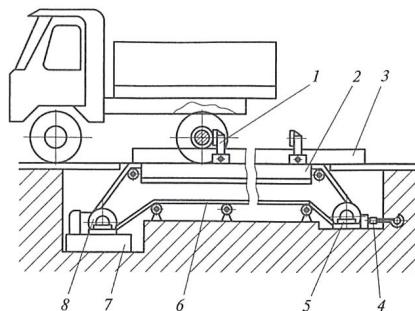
Схема толкающего конвейера: 1 – толкатель; 2 – направляющие пути тягового органа; 3 – колесоотбойник; 4 – натяжной механизм; 5 – натяжная станция; 6 – тяговый орган; 7 – приводная станция; 8 – ведущая звездочка
